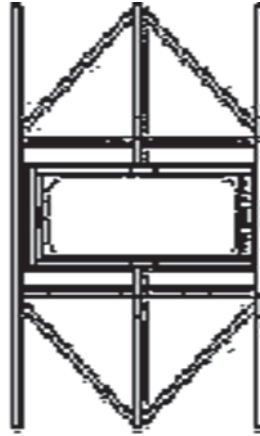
Bloco construtivo componente (1) do subsistema rodado dianteiro
